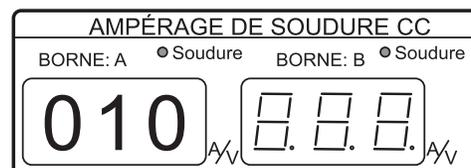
Compteur de soudage à CC (compte à rebours)
